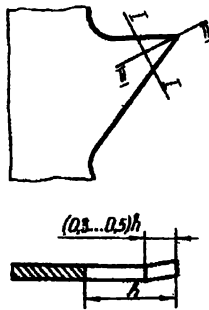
Форма вершины зуба узкой ленточной пилы после развода
